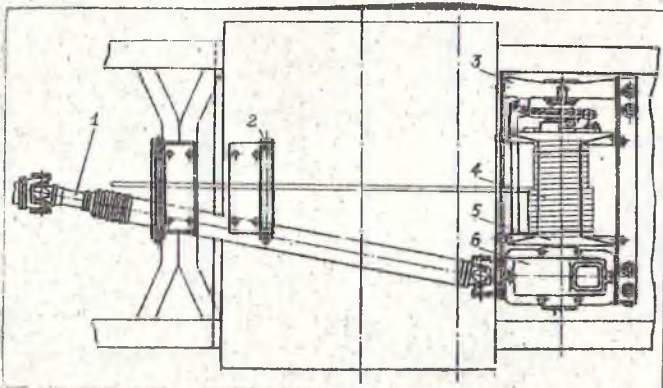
Установка лебедки на раме лесовозного оборудования: 1-карданный вал привода лебедки; 2-ролик; 3-траверса; 4-трос; 5-барабан; 6-редуктор.
